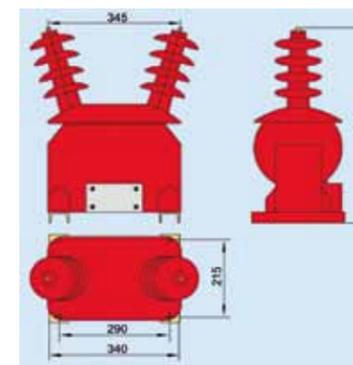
Внешний вид и размеры трансформатора напряжения JDZXW-20
